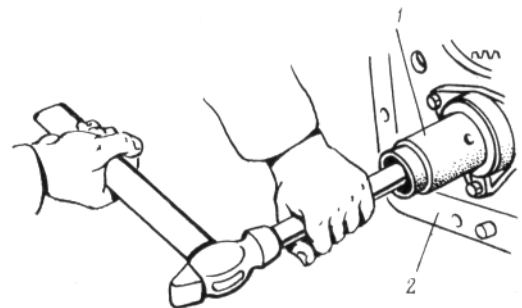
Випресування внутрішнього вала: 1- гніздо внутрішнього вала; 2- корпус коробки передач
